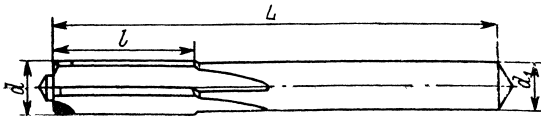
Развертки цилиндрические твердосплавные фирмы «Хам» (ФРГ)
